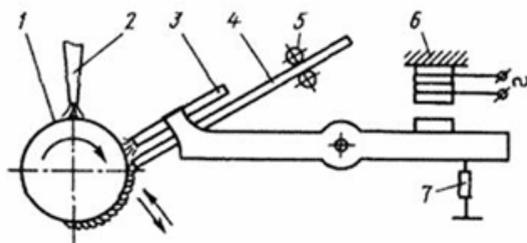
Схема вибродуговой наплавки: 1 – наплавляемое изделие; 2 – сопло для подачи охлаждающей изделие жидкости; 3 – сопло для подачи жидкости в зону сварки; 4 – электродная проволока; 5 – подающие ролики; 6 – электромагнитный вибратор; 7 – пружина
